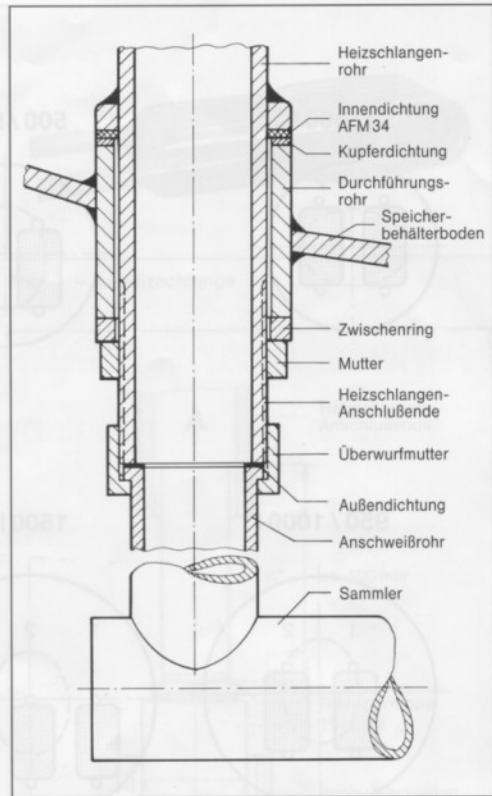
Durchführungsrohr mit Heizschlangenanschlußende und Sammler – L-Speicher
